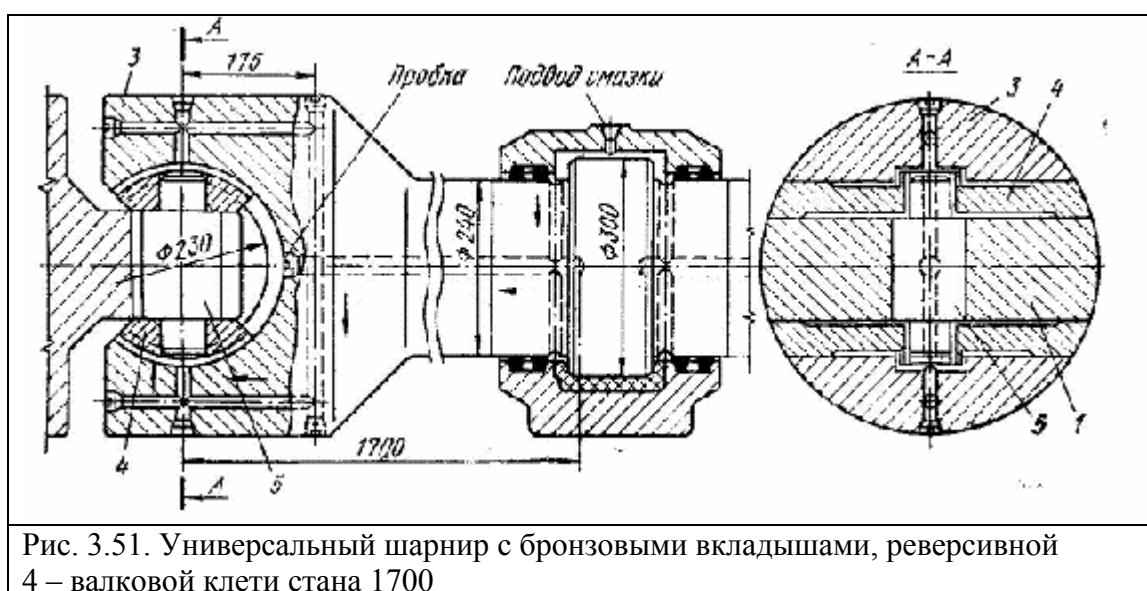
Универсальный шарнир с бронзовыми вкладышами, реверсивной 4 – валковой клетки стана 1700
